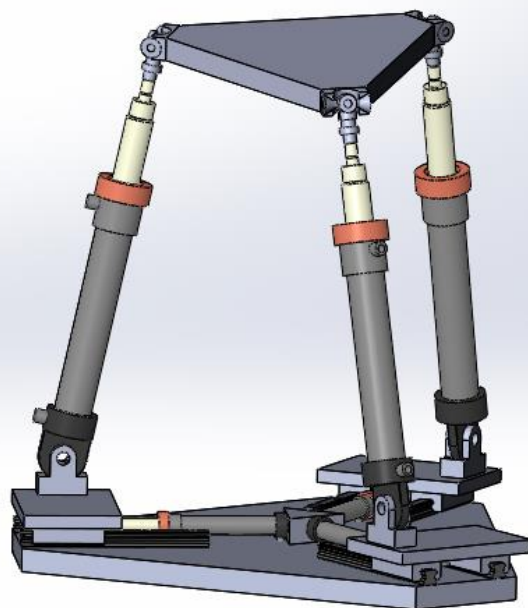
3D CAD модель нового трипода вида 3-PRPS.
